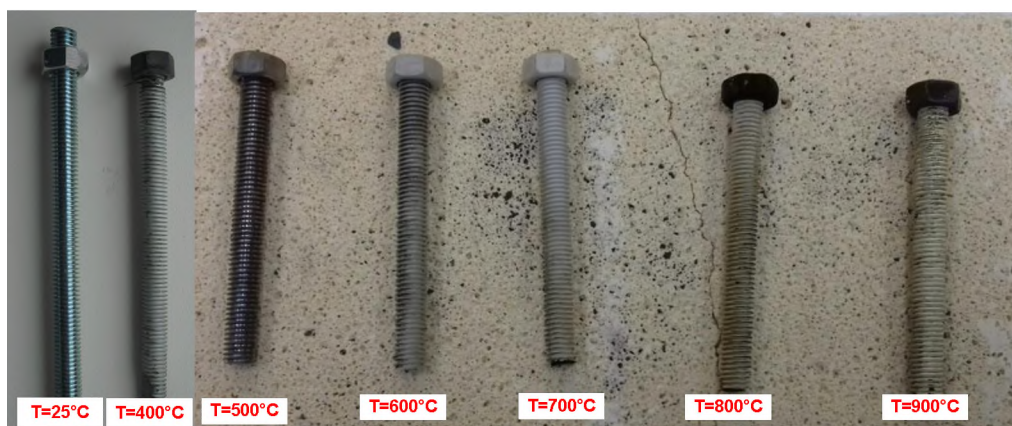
Резьбовая пара шпилька М8-гайка при различных температурах нагрева
